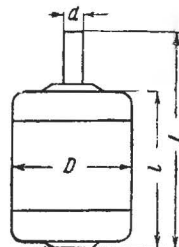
Обозначения размеров электродвигателя (к таблице 2).
